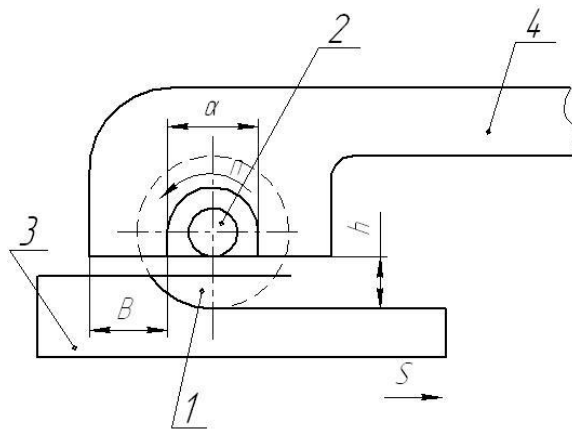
Схема дії місцевого вентиляційного відсмоктувача: 1 – фреза; 2 – посадочний вал; 3 – заготовка; 4 – відсмоктувач.
